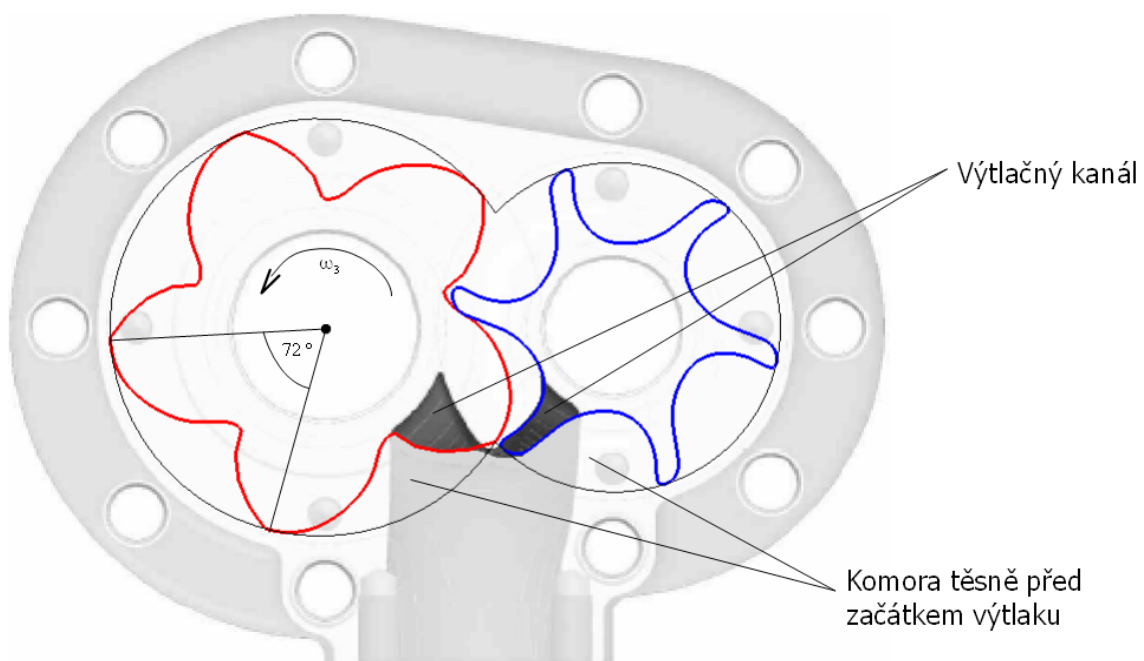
Profil zubu vedlejšího rotoru a profil zubu hlavního rotoru
